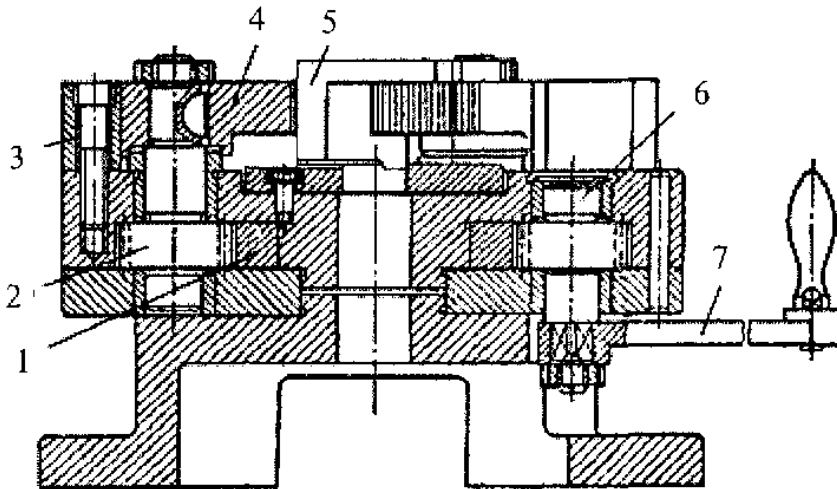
Стаціонарний пристрій без кондукторної плити
